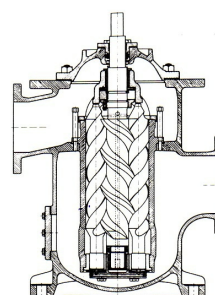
viser en 3-spindlet skrue-pumpe.
